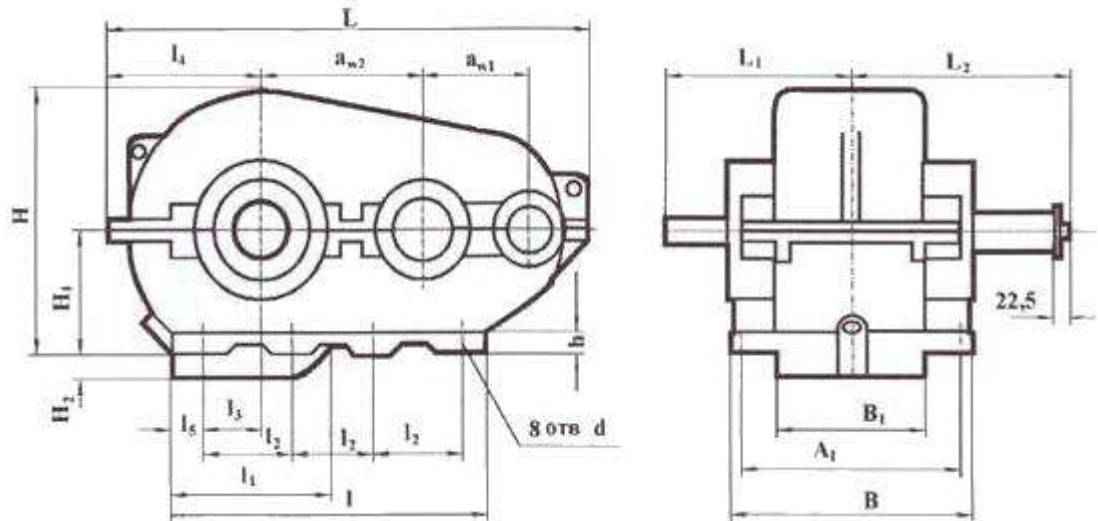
Ескіз редуктора РК600-50-22М-48
